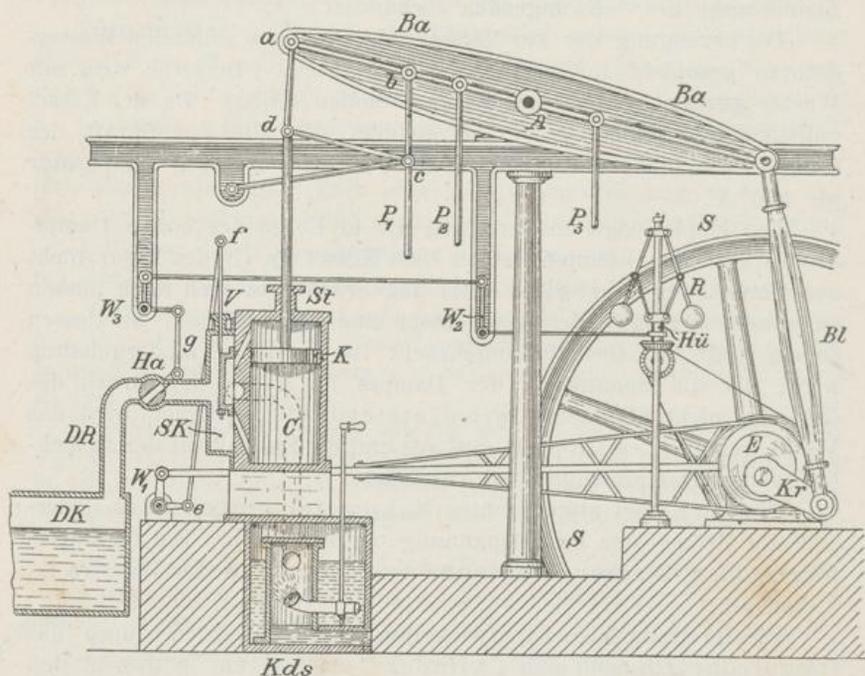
Dampfmaschine (Niederdruckmaschine).
